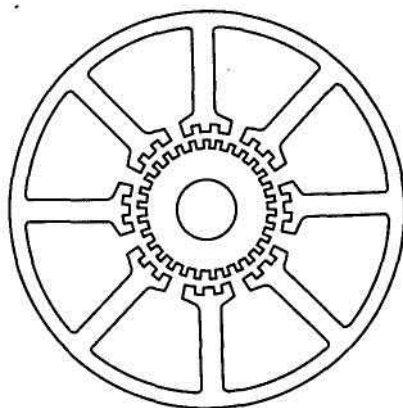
Листы стали статора и ротора шагового двигателя индукторного типа
